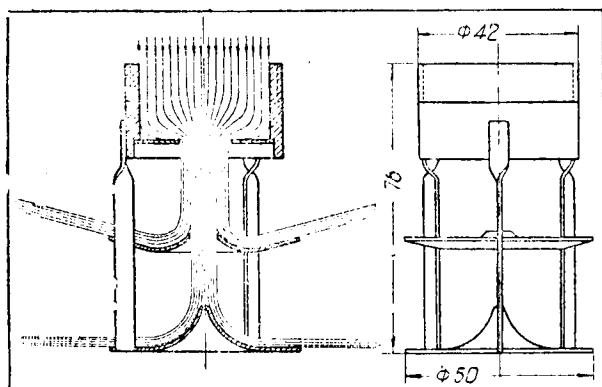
Насадка конькового агрегата. Общий вид и схема разбрызгивания воды.
